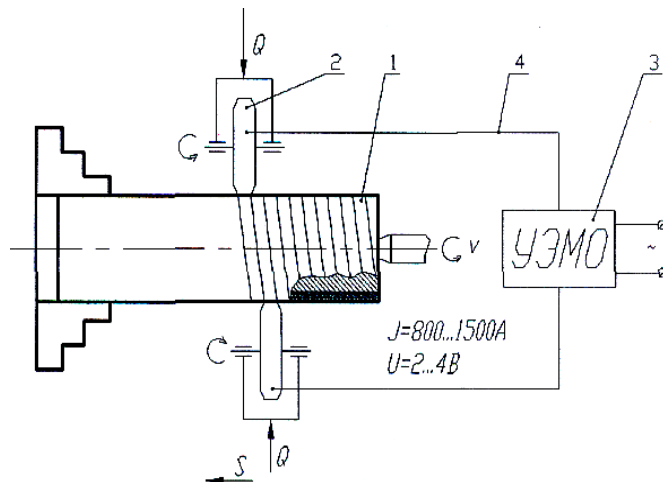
Закалка посадочных мест под подшипники качения вала-шестерни на токарно-винторезном станке.
